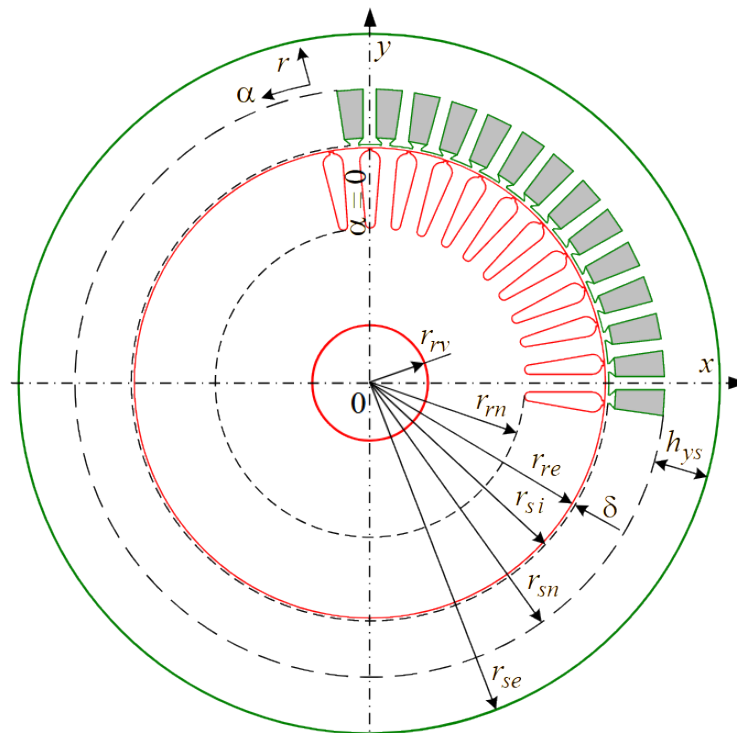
Конструкторська розрахункова модель ТАД
